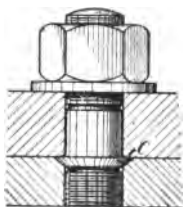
Stiftschrauben mit Bund zum Verstemmen.
